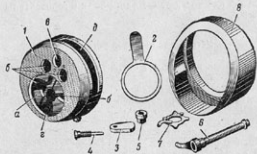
Шар в разобранном виде и цилиндр защиты: 1 — шар; 2 — зажимное кольцо с рукояткой; 3 — заслонка; 4 — стержень заслонки с пружиной; 5 — ступка стержня заслонки; 6 — передняя трубка телескопического прицела; 7 — обшивка трубки телескопического прицела; 8 — цилиндр защиты шара; а — гнездо для зажимного кольца с рукояткой; б — отверстия для винтов, соединяющих шар с защитой шара; в — отверстие для прицеливания; г — отверстие для пулемета; д — вырез для заслонки
